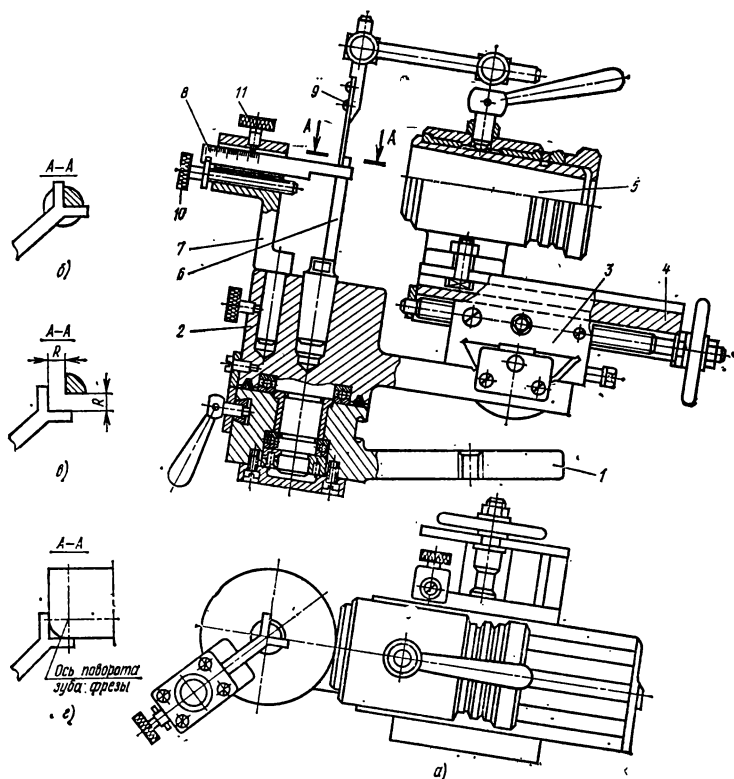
Приспособление для заточки концевого инструмента по радиусу
